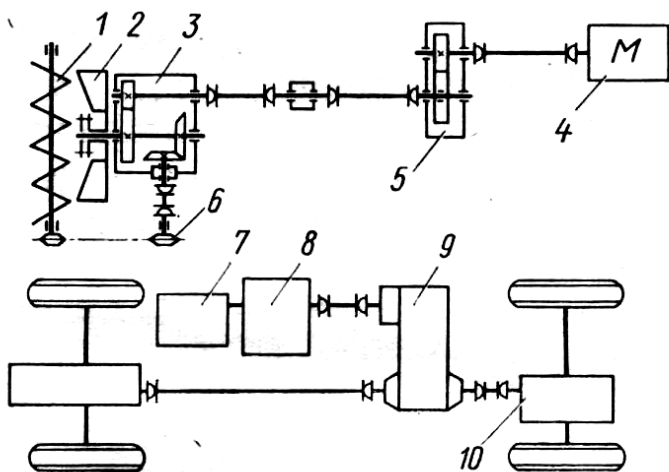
Кинематическая схема двухмоторного шнеко-роторного снегоочистителя:
